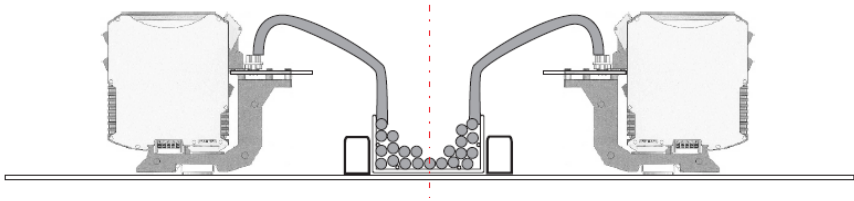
Sicht (Querschnitt) auf die pac-Träger mit Kabelkanal
